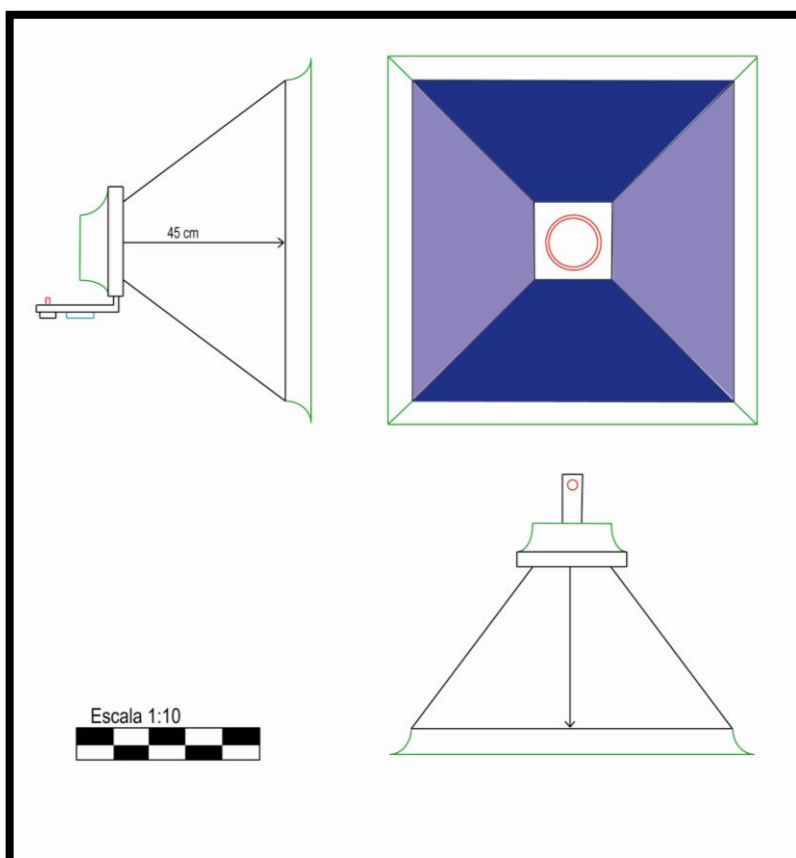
Imagen en alzado, planta y perfil del prototipo diseñado.
